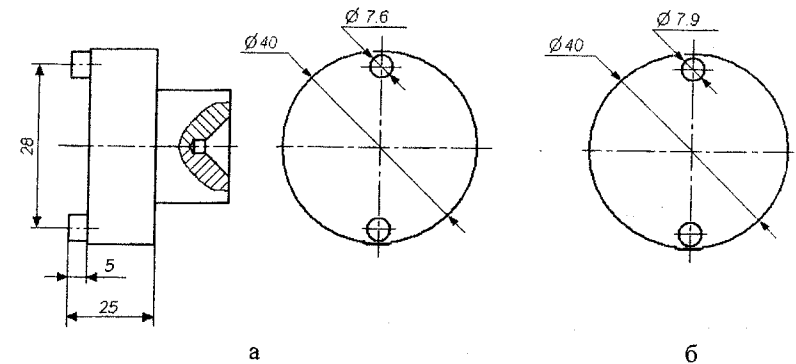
Установочные приспособления: а – для чернового точения; б – для чистового точения
